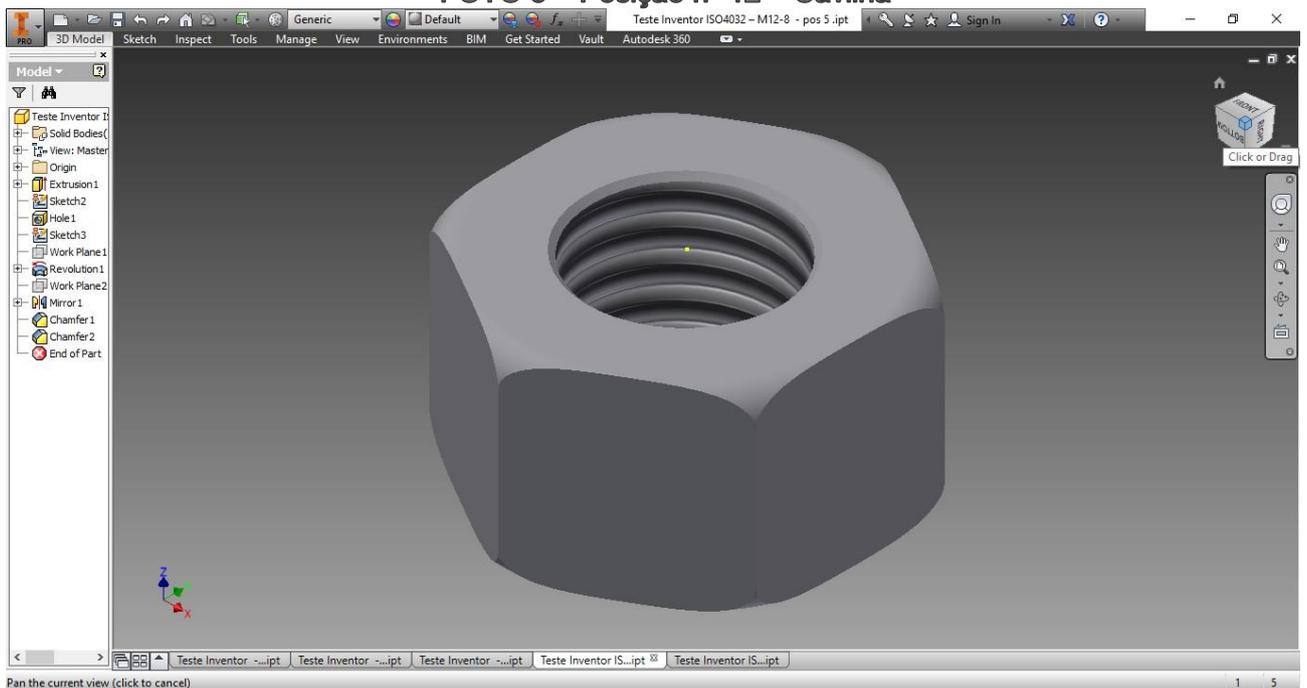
Posição nº 5 – Porca ISSO 4032 – M12-8
